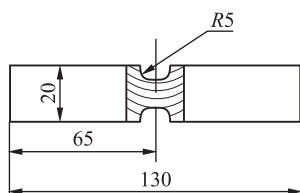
Образец для определения прочности металла шва, выполненного СТП
